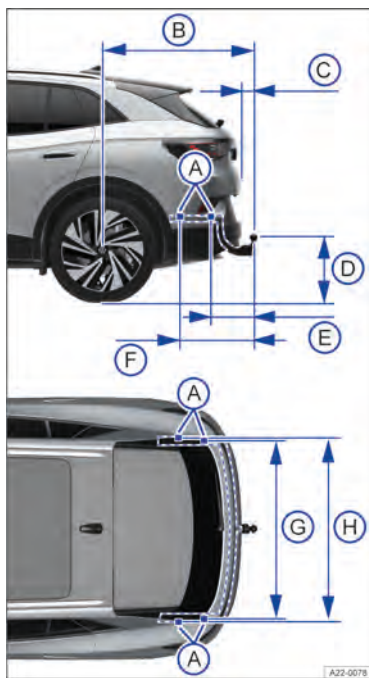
Dimensões e pontos de fixação para instalar um dispositivo de reboque posteriormente.
